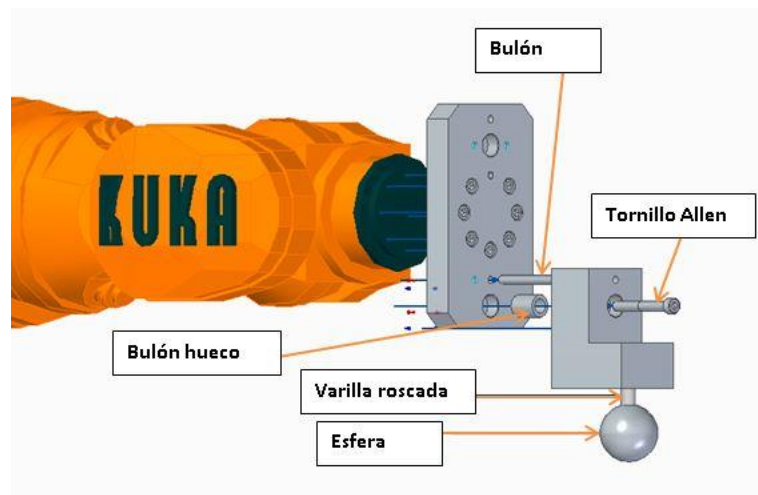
Proceso de montaje del "Utillaje bola" sobre la "Placa brida" y sus componentes.
